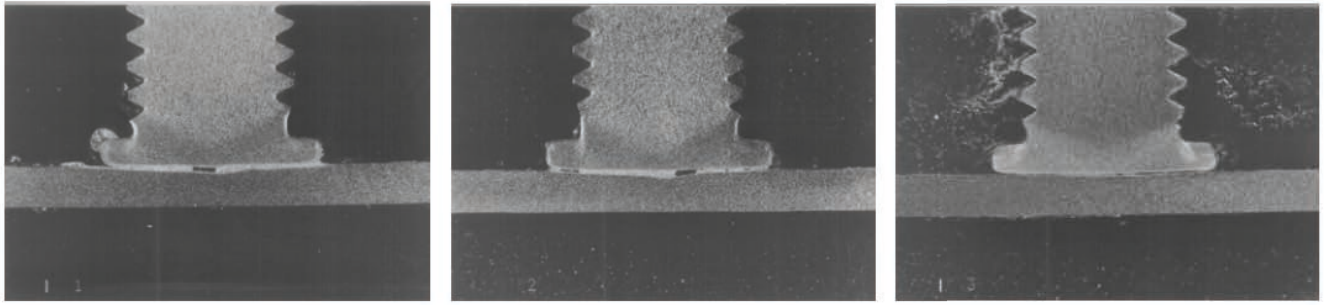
Schliffbild einer Kurzzzeitschweißung auf verzinktem Blech ohne Schweißbadschutz
